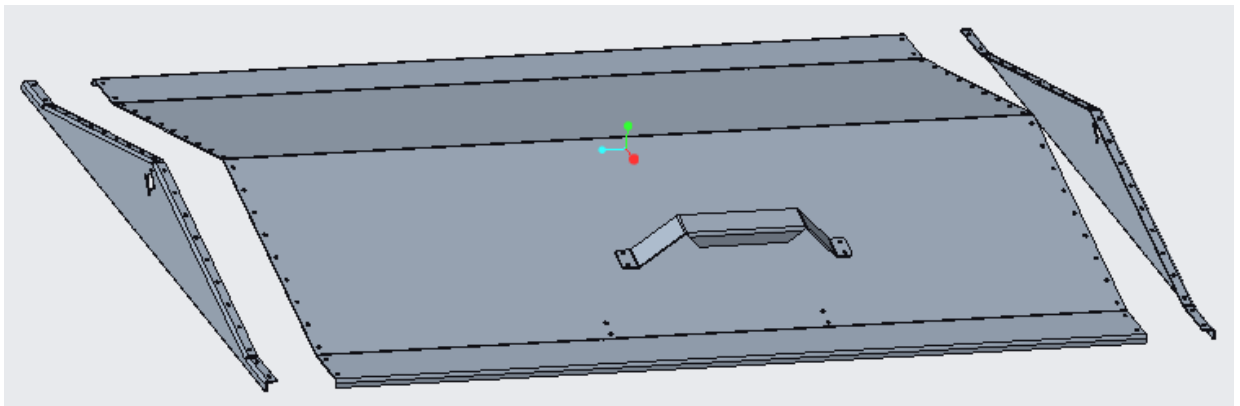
Peces que formen la tapa de la tremuja. Font: Pròpia
